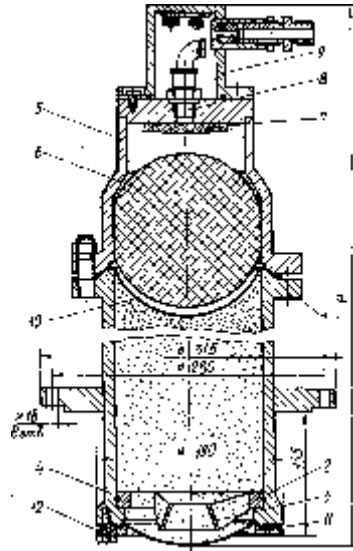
Порошковий полум'япридушувач: 1 – корпус; 2 – вогнегасний склад; 3 – розпилювач; 4 – пружинне кільце; 5 – кожух; 6 – поршень-куля; 7 – пороховий заряд; 8 – піропатрон; 9 – кришка вступного пристрою; 10, 11 – мембрани; 12 – фланець
